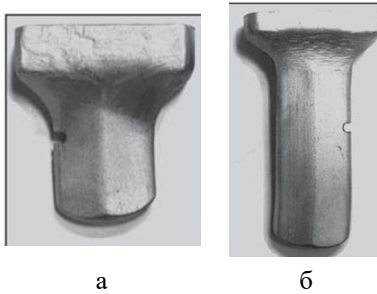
Дефекти видавлених заготовок, спричинені неправильним налаштуванням величини ходу пуансона при деформації заготовки лопатки
